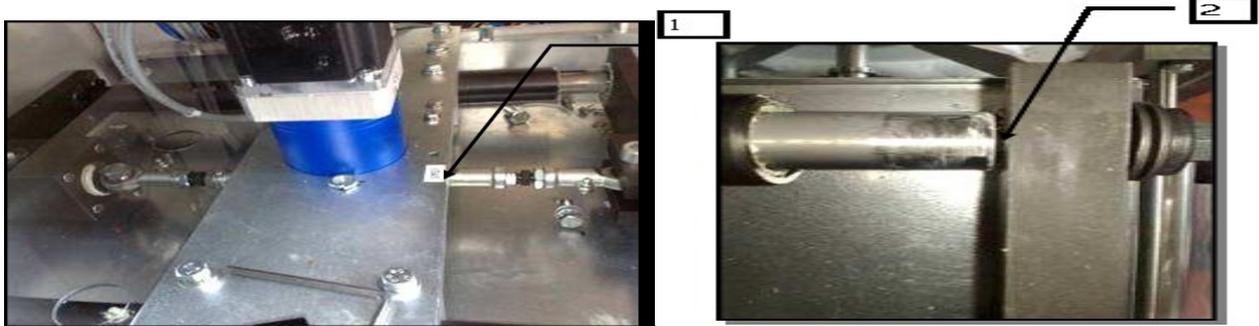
Réglage de la pression de soudure .
